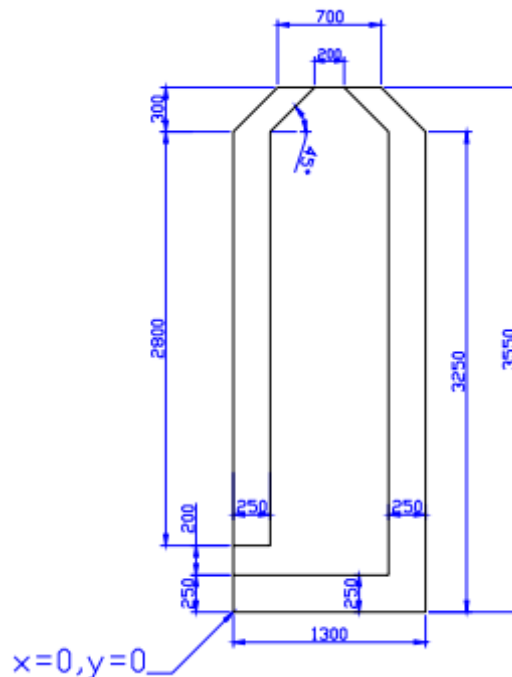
Estrutura e Dimensões do Combustor (AUTORES)
